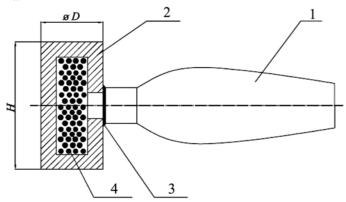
Малоинерционный медицинский молоток: 1 – ручка; 2 – основная часть; 3 – сварка; 4 – стальные шарики
